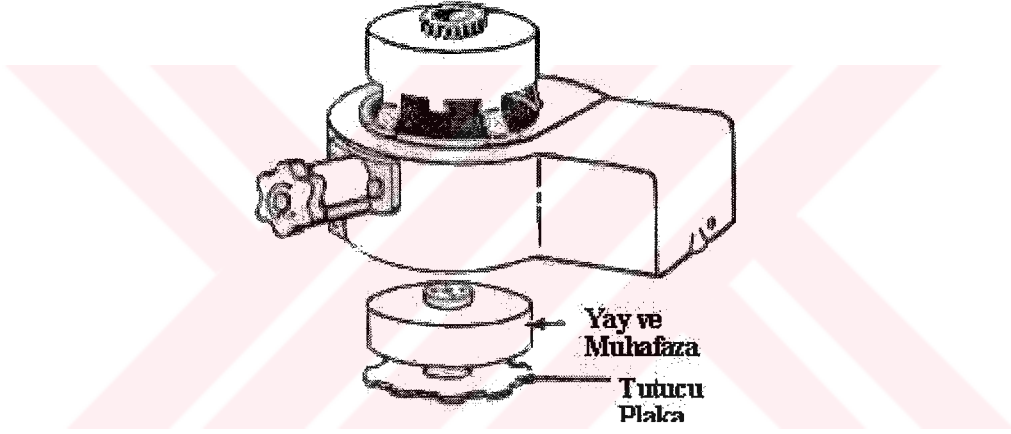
Ayak ile ilk hareket düzeneği (Miller & Miller, 1993)
